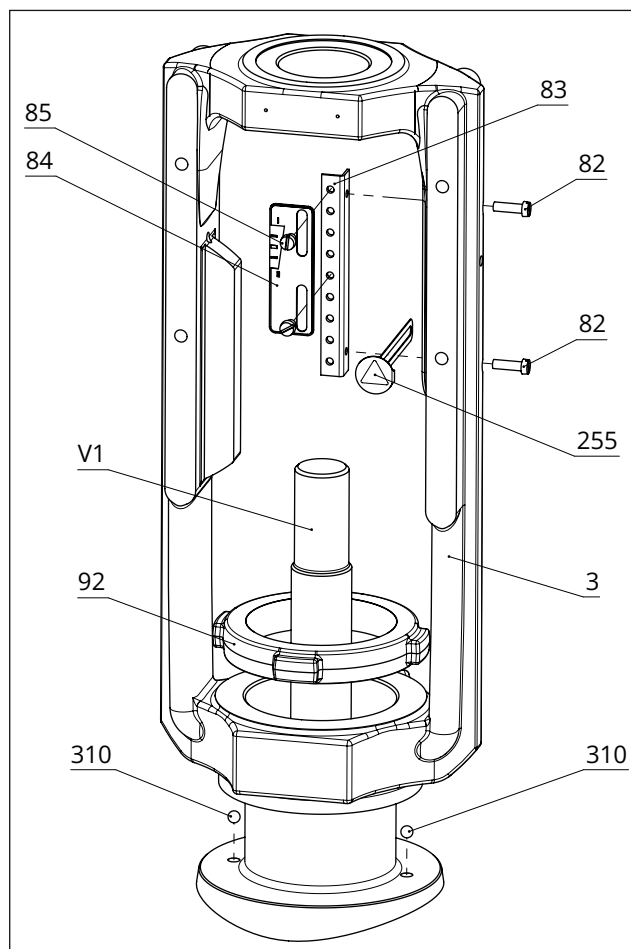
Montageübersicht der Baugruppe Joch mit Hubschild in der Standardausführung
